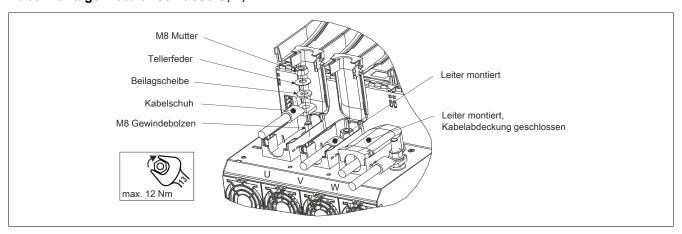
Kabelmontage Motoranschlüsse U, V, W
